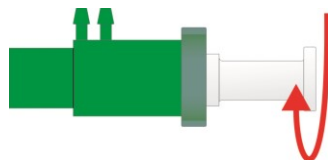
Montagewerkzeug im Uhrzeigersinn drehen
